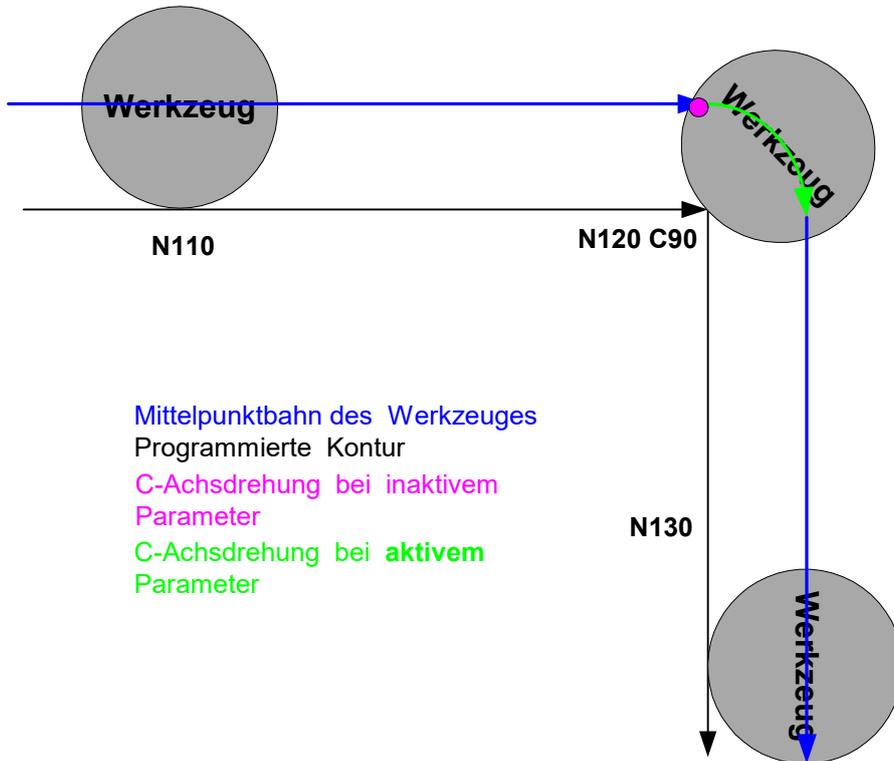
Prinzipieller Bewegungsablauf einer C-Achse mit G26
